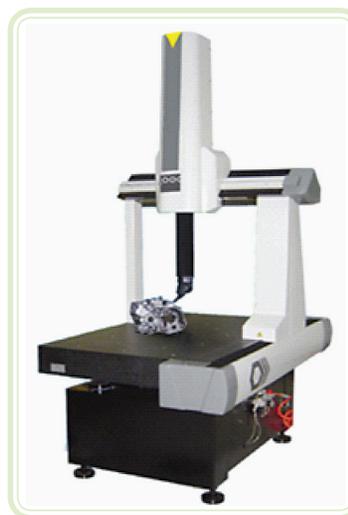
Máquina de medir por coordenadas Inspector BR, produzido pela empresa Hexagon Metrology
